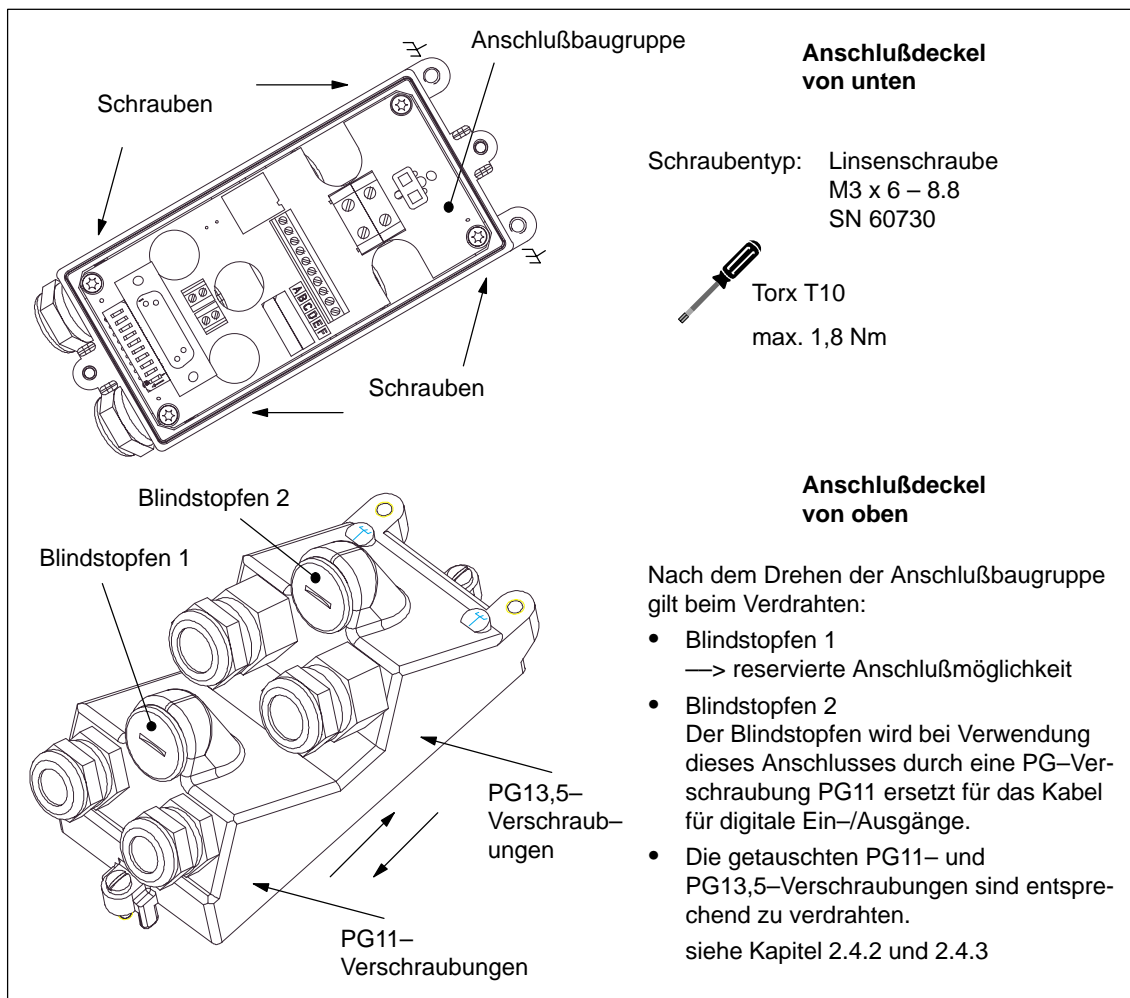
Anschlußdeckel: Kabelabgangsrichtung ändern
